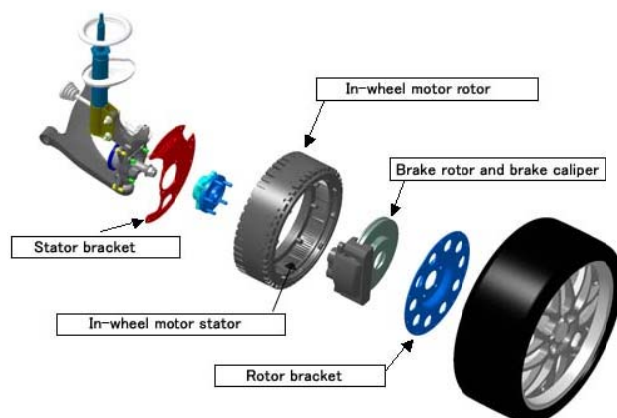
Esquema de montagem dos constituintes do motor na roda
